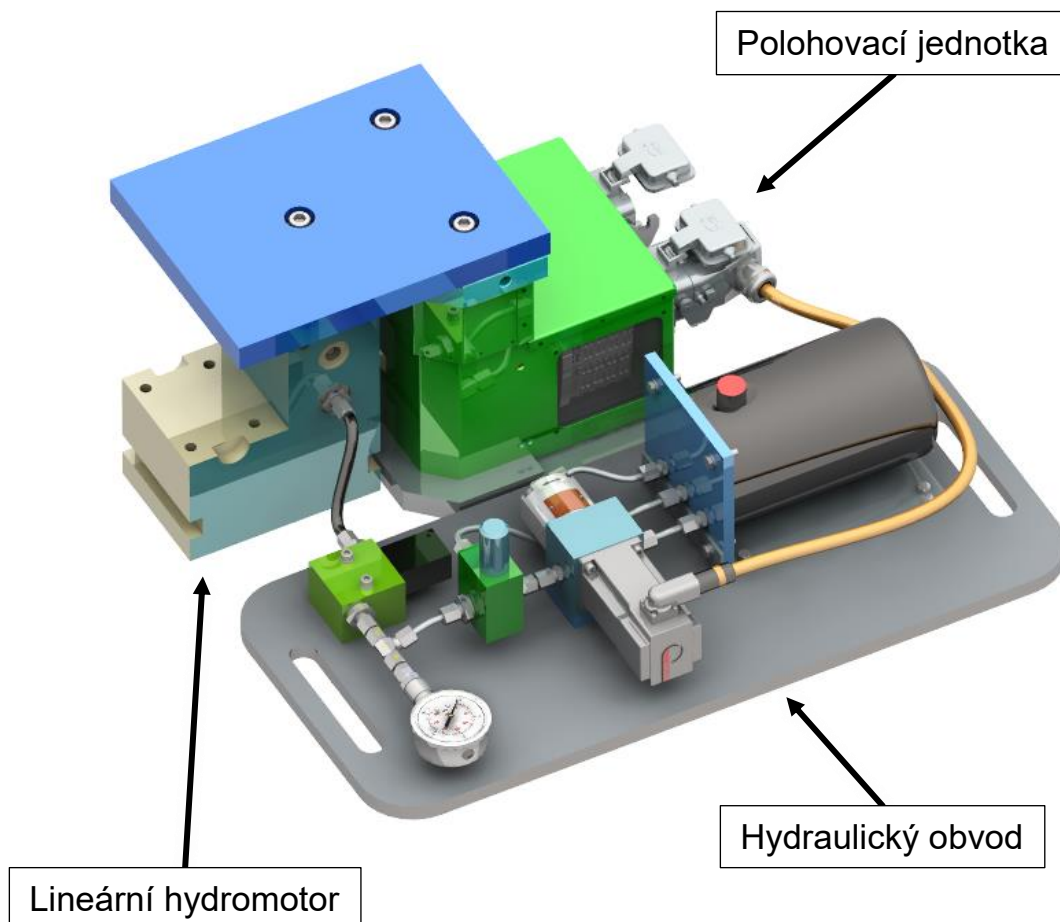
Návrh 2 – Elektro-hydraulický aktuátor
